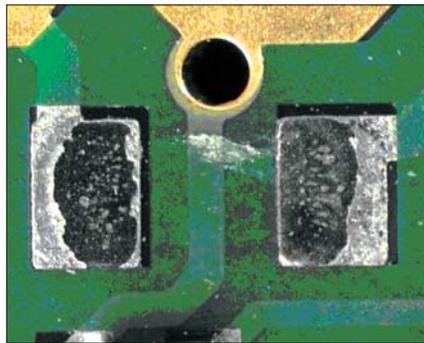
Abgetrenntes Bauelement hinterlässt dunkle Padoberflächen
